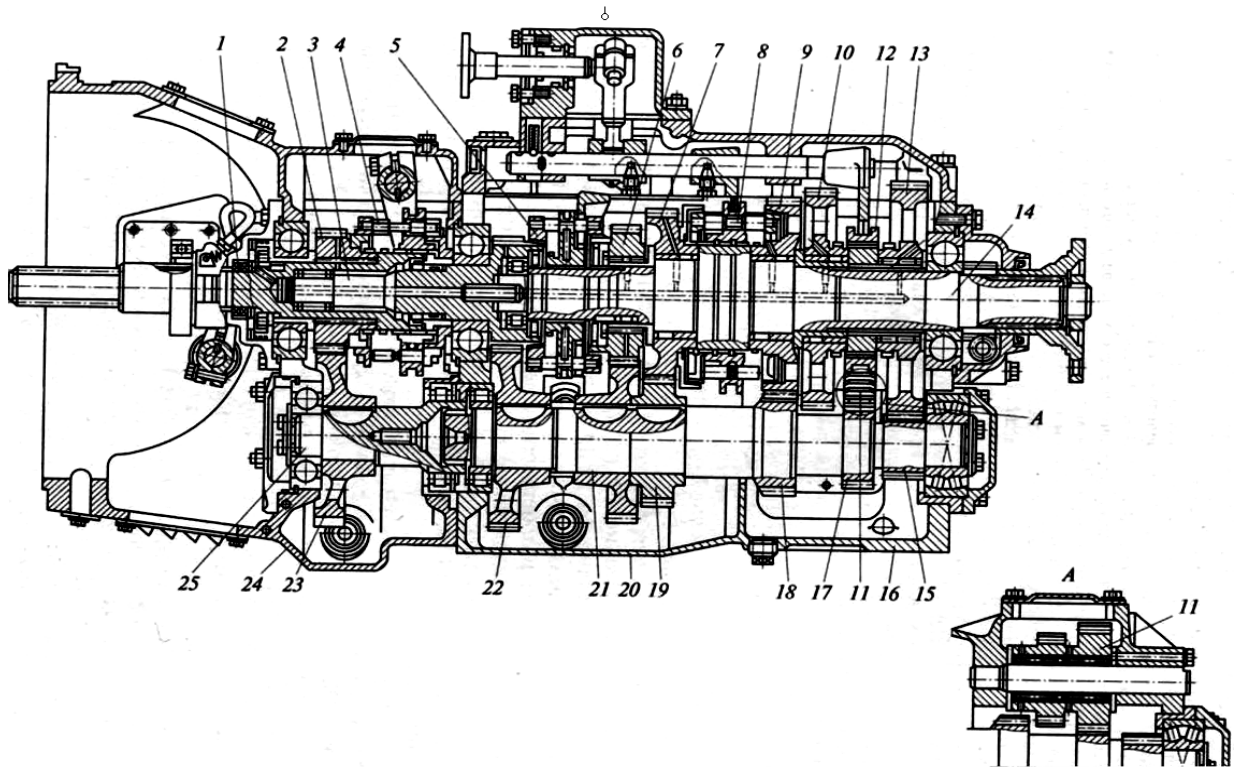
Коробка передач автомобиля КАМАЗ-5320:
